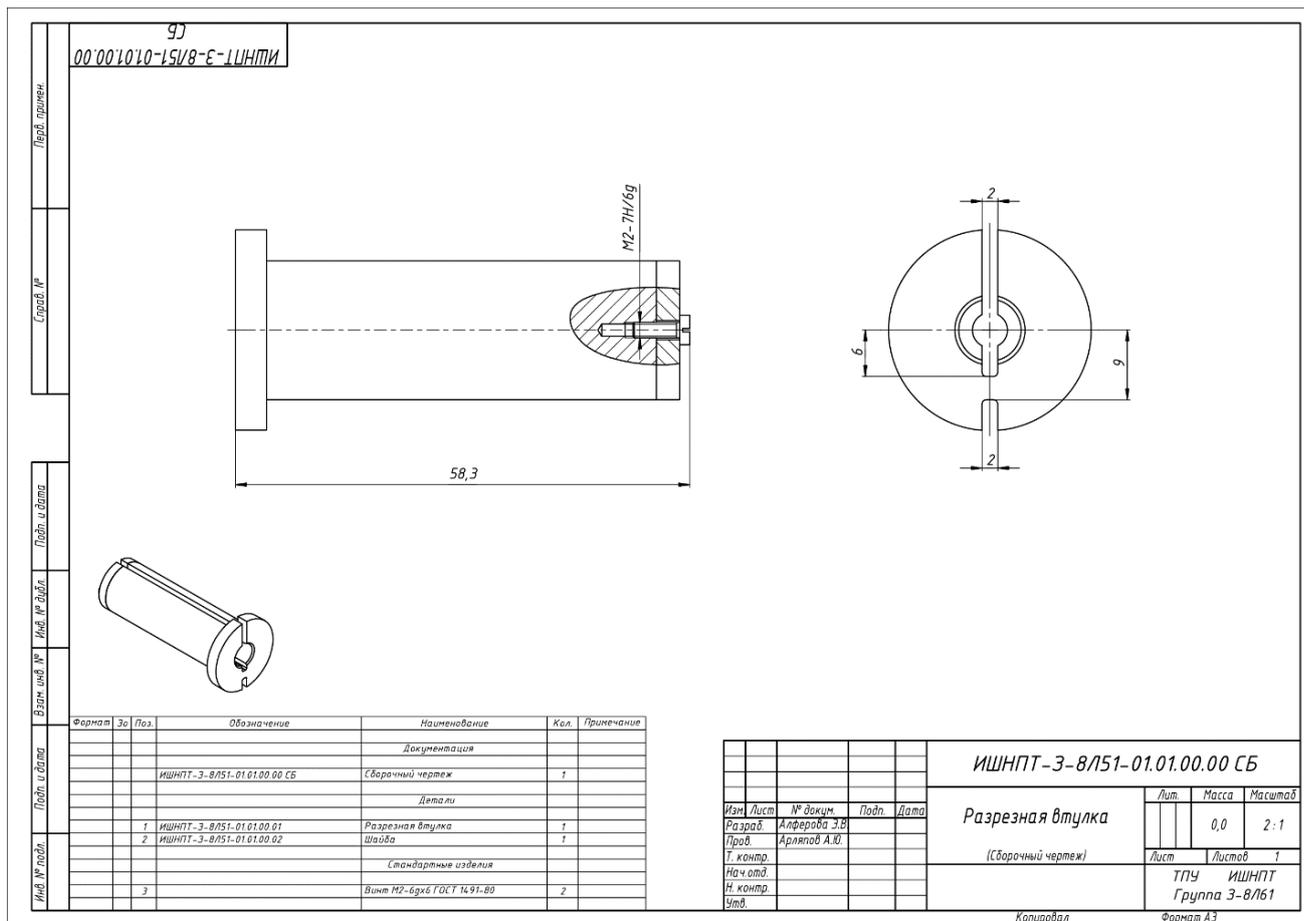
Чертеж разрезной втулки для токарной операции.
